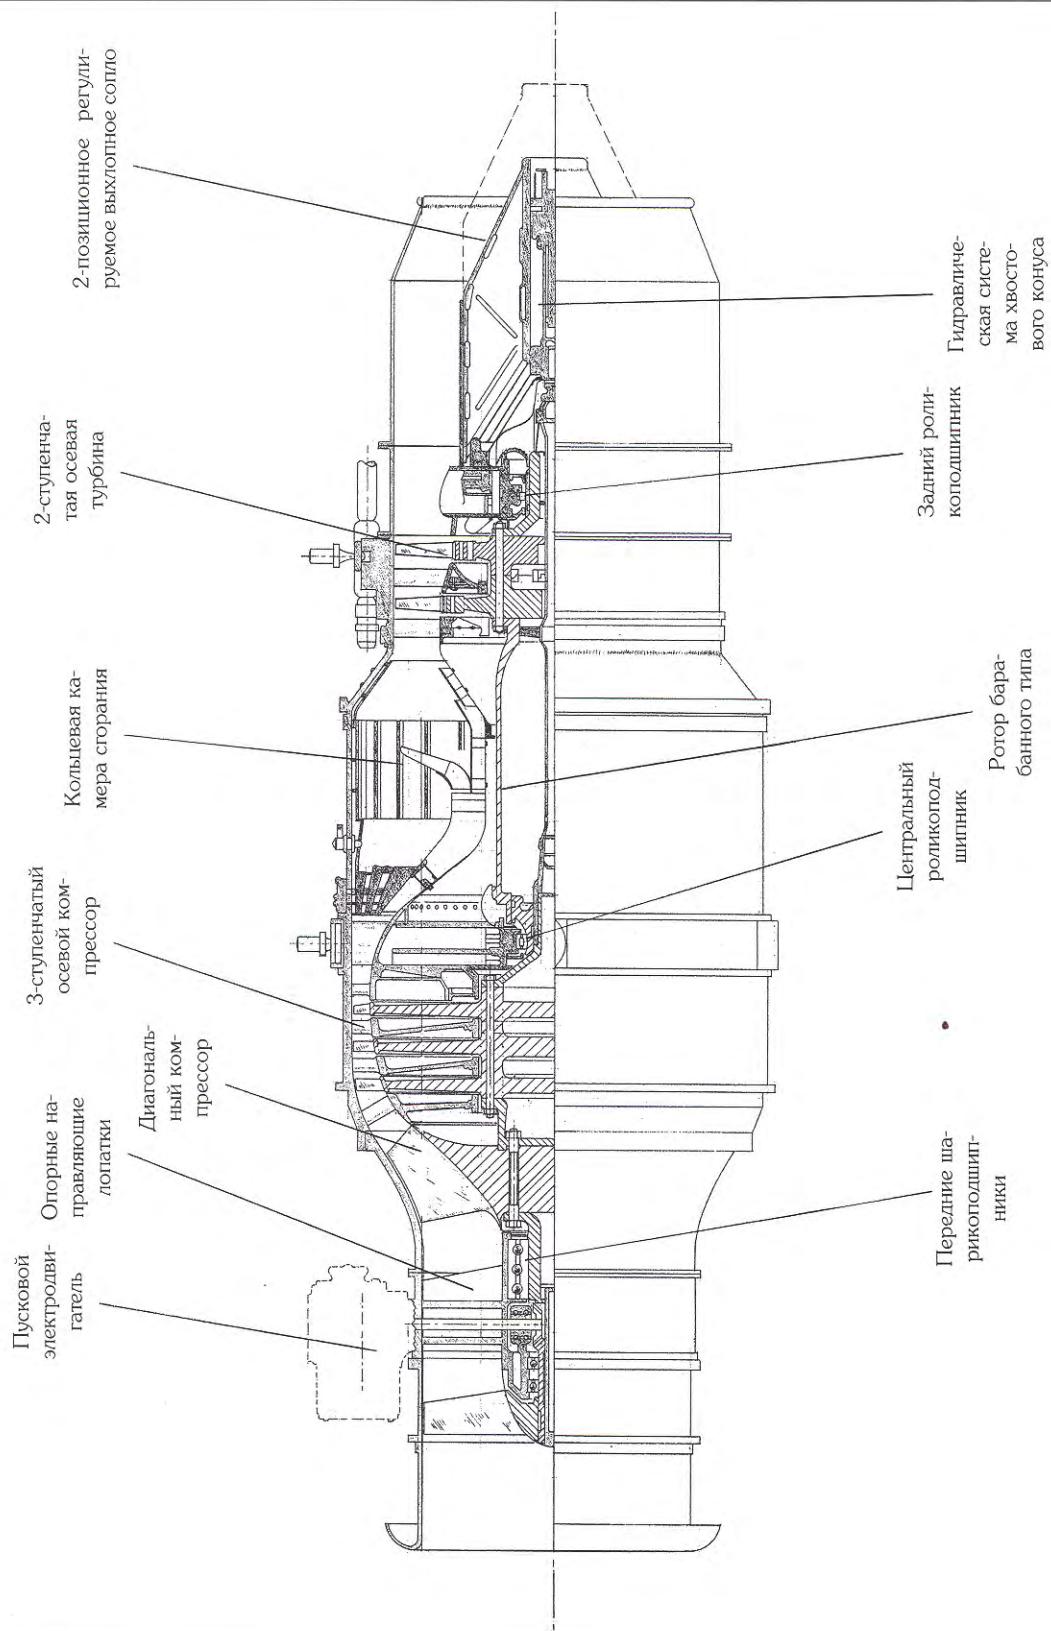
Турбореактивный двигатель HeS 011 (109-011 V1) (схема выполнена автором)
